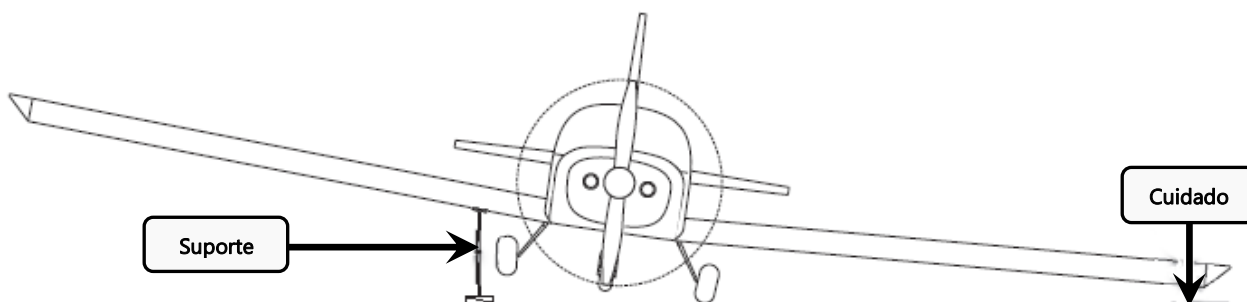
Instalação do suporte para instalação do trem de pouso principal
